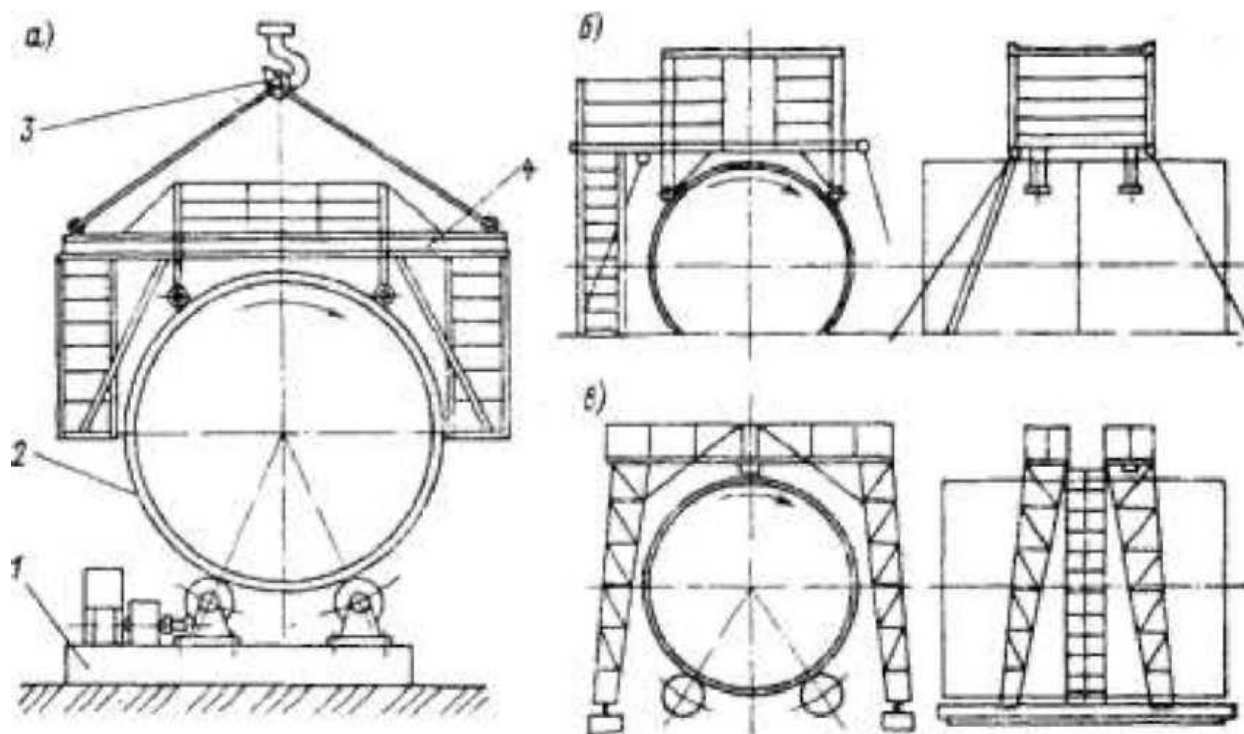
Установка для сварки кольцевых стыков блоков цементных печей: *а* – сварочная площадка удерживается краном; *б* – сварочная площадка удерживается расчалками; *в* – с передвижными мостиками
